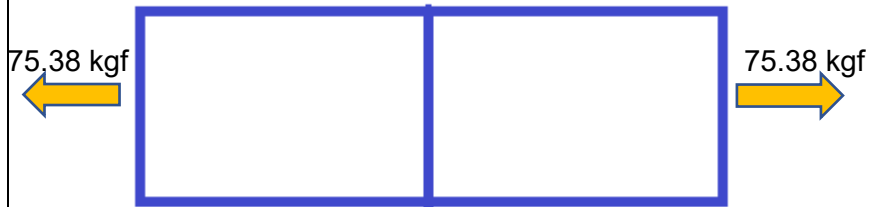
Análisis de esfuerzo cordón de soldadura
